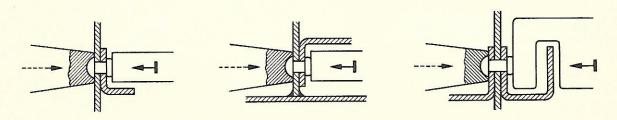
Anwendung der Vorhaltewerkzeuge
